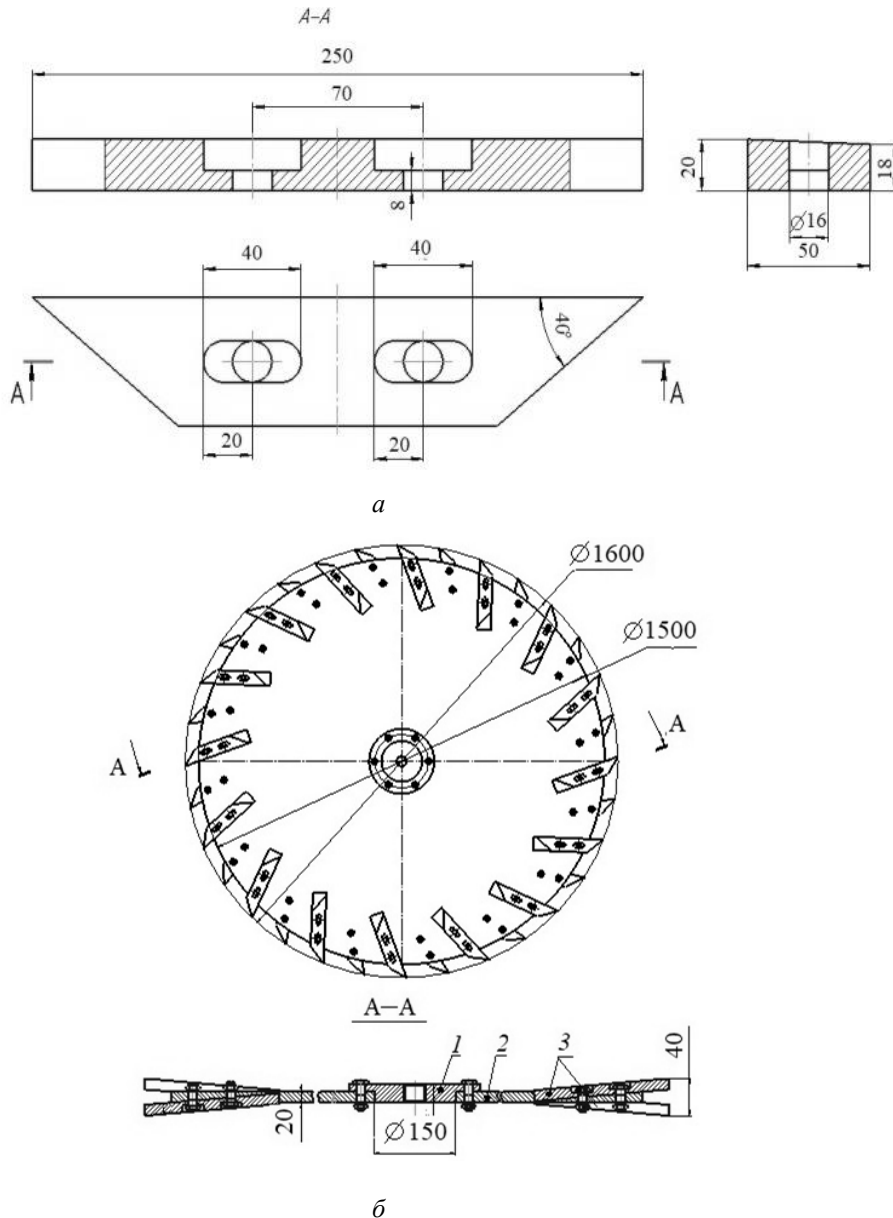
Чертеж резца (а, вид сверху) и фрезы (б):
